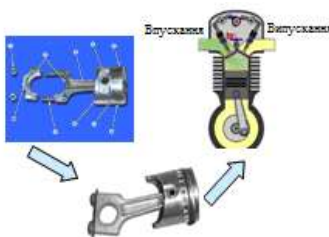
Складений шатуно-поршневий вузол, двигун
